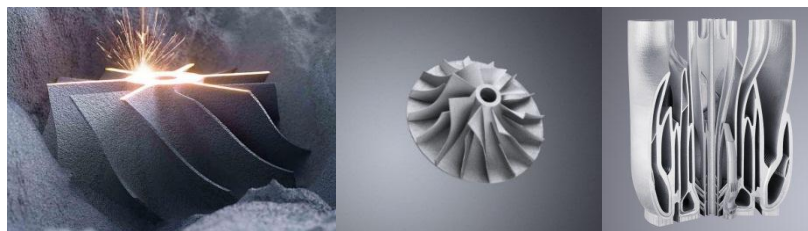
Piezas manufacturadas con impresión metálica en 3D
